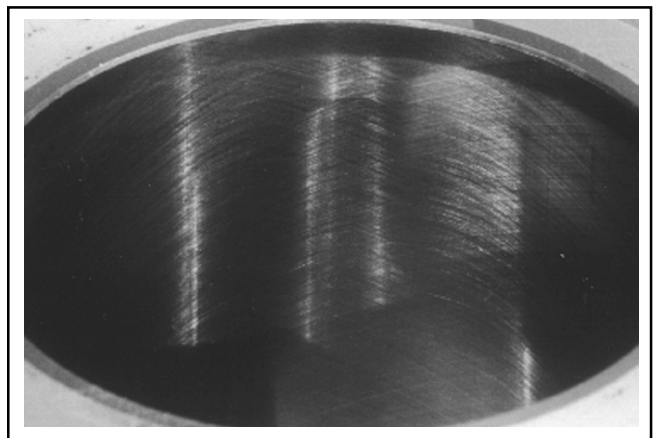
Aspetto dell'alesaggio dopo l'alesatura.
